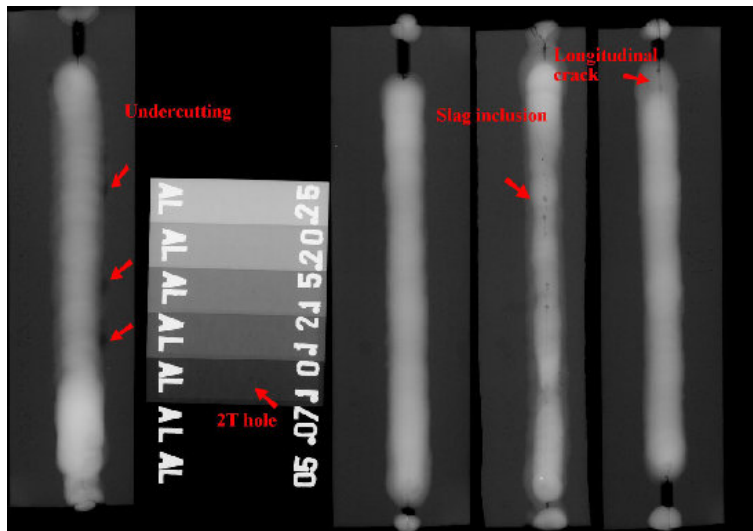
Fotografía que muestra distintos porcentajes de penetración que tuvo un ICI en unos cordones de soldadura.
